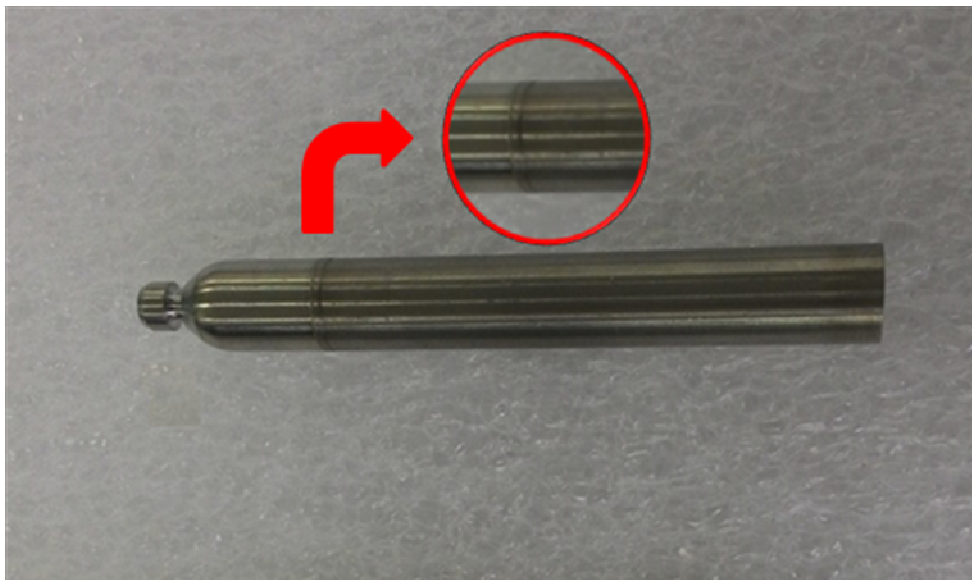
CP soldado por resistência e pressão aprovado
